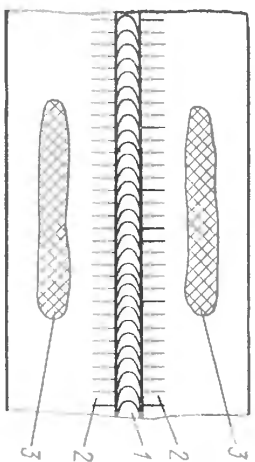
Расположение зон нагрева: 1 — сварной шов, 2 — зоны растяжения, 3 — зоны нагрева
